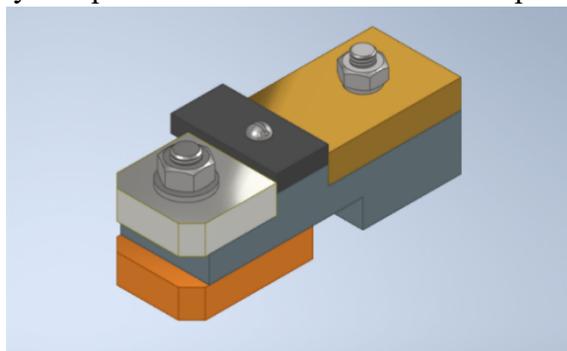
3D-модель сборочного узла «Соединения резьбовые»
